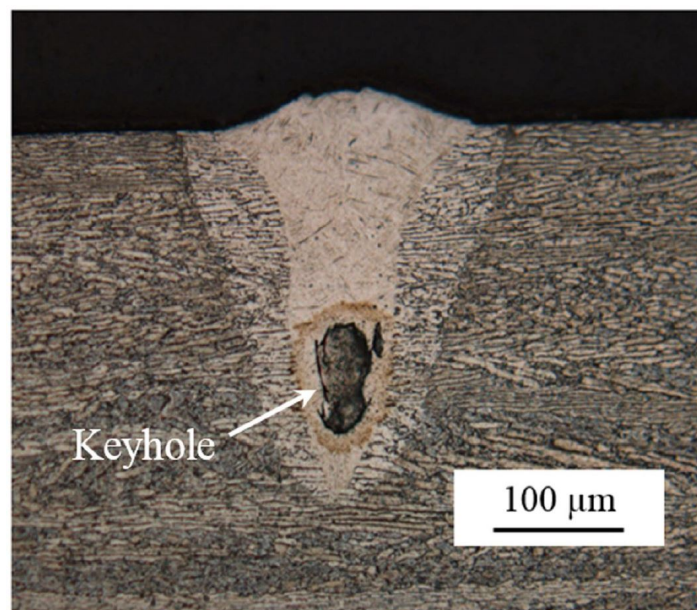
Illustration d'une porosité formée au cours du procédé de soudage laser. Extrait de Gong et al. [34]
